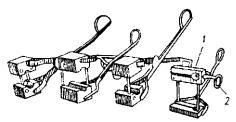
Формы для стеклодувных изделий: 1— корпус формы; 2—держатель для разъема и соединения.
